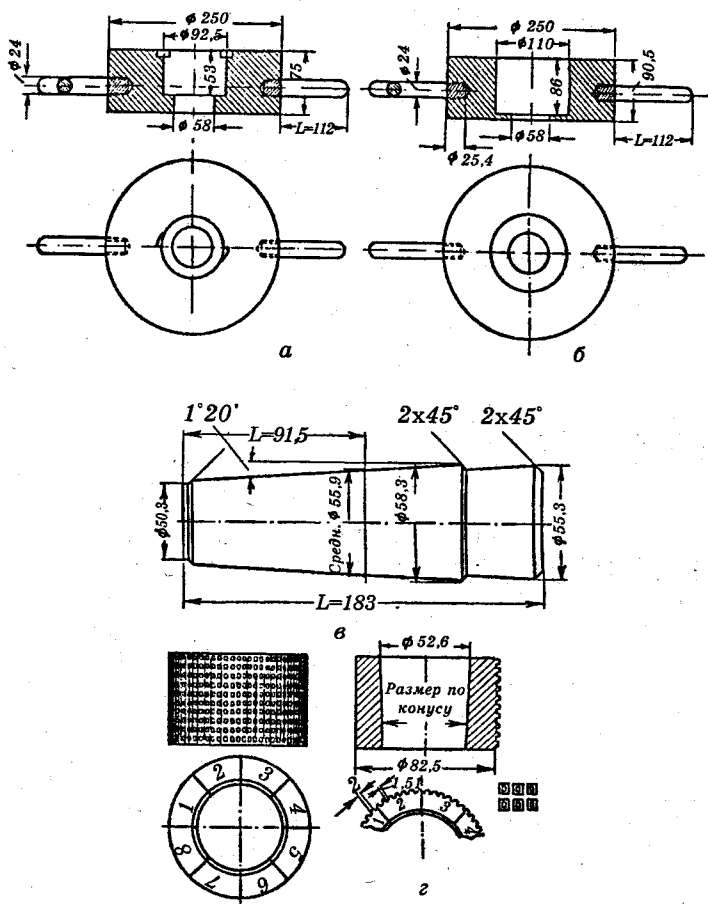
Детали приспособления для опрессовки вкладышей двигателя:
